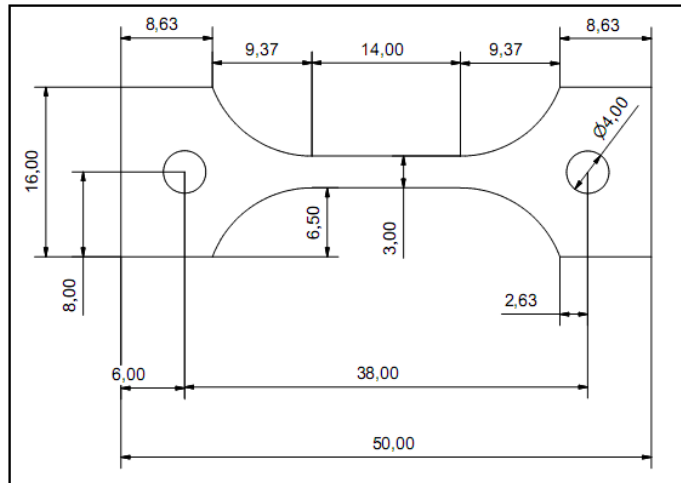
10 Plano de la probeta para ensayo de tracción.
